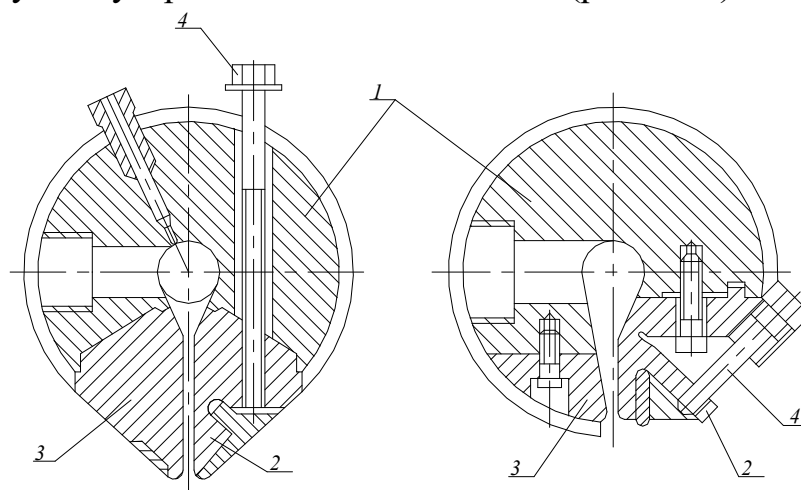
Головки для виробництва тонких плівок: 1 – корпус, 2 – верхня регульована губка, 3 – нерухома губка, 4 – регулювальний болт
